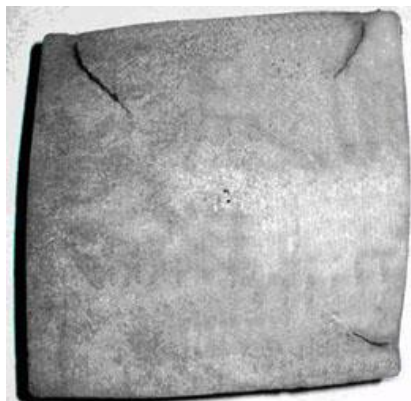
Поперечное сечение сортовой заготовки с повышенной ромбичностью и внутренними трещинами
